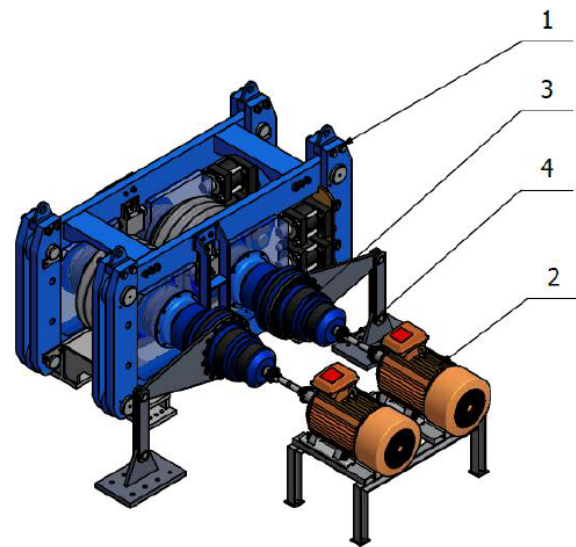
Модель, що ілюструє циліндричний прес із приводом двох роликів: 1 – рама робочих валків, 2 – електродвигун dSg315S6-EP, 3 – планетарні редуктори SL18003 з реакційним кронштейном, 4 – шарнірний з'єднувач [2]
